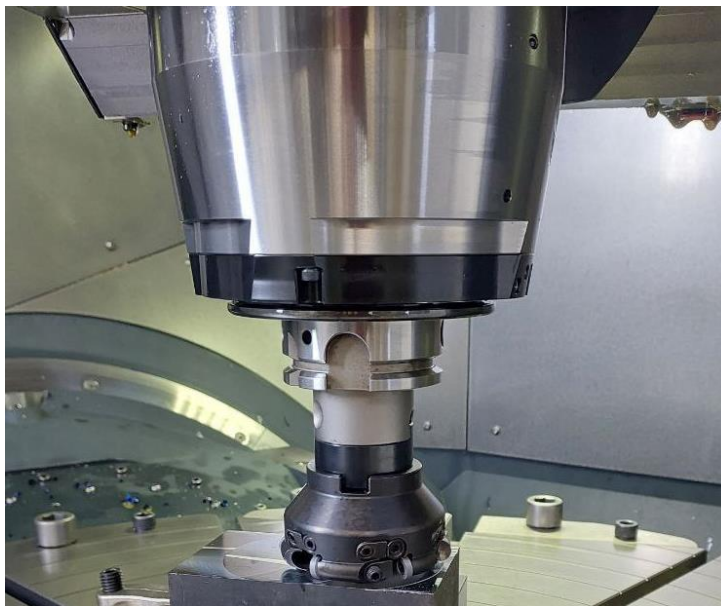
Торцева фреза SECO TOOLS діаметром 63 мм
